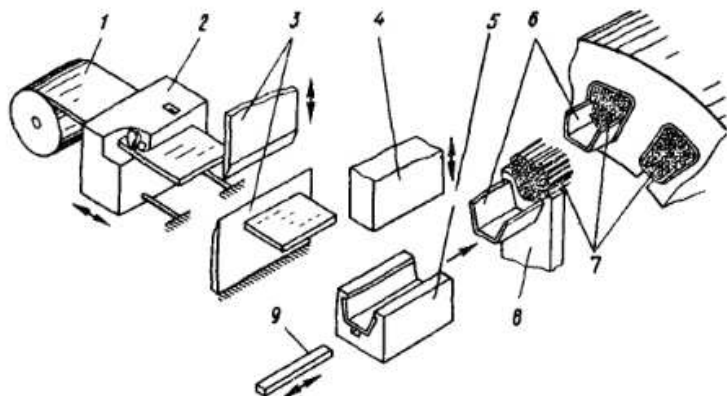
Схема работы станка для заклинивания пазов статора (пазовые крышки из широкой ленты)
